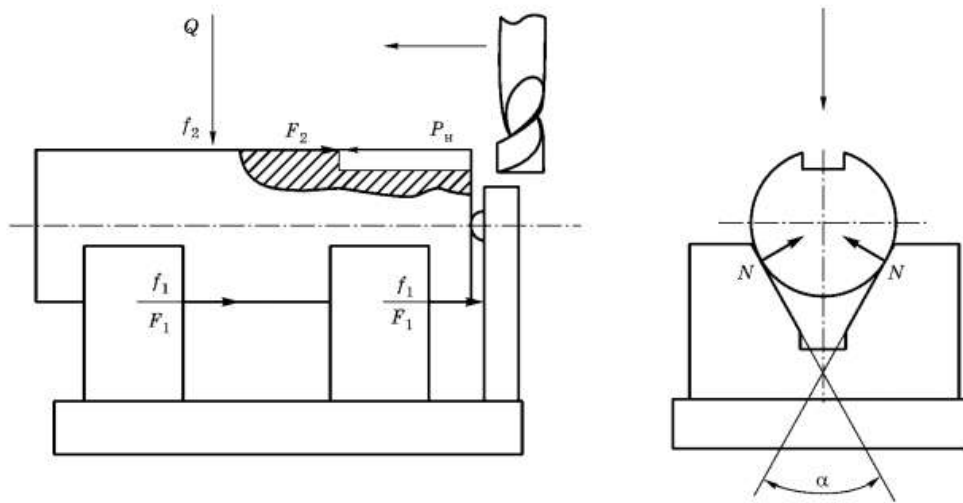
Схема фрезерованию шпоночного паза концевой фрезой
